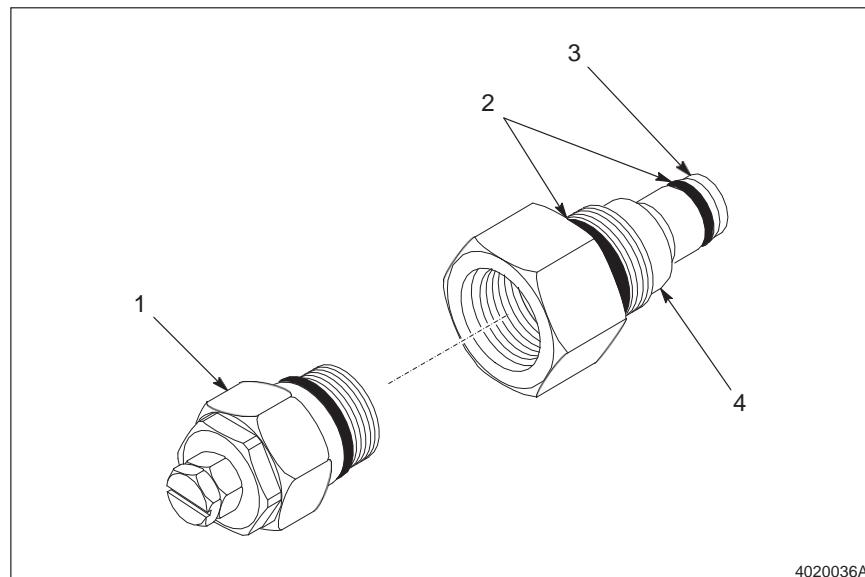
Separando o Conjunto Atuador do Corpo da Válvula
